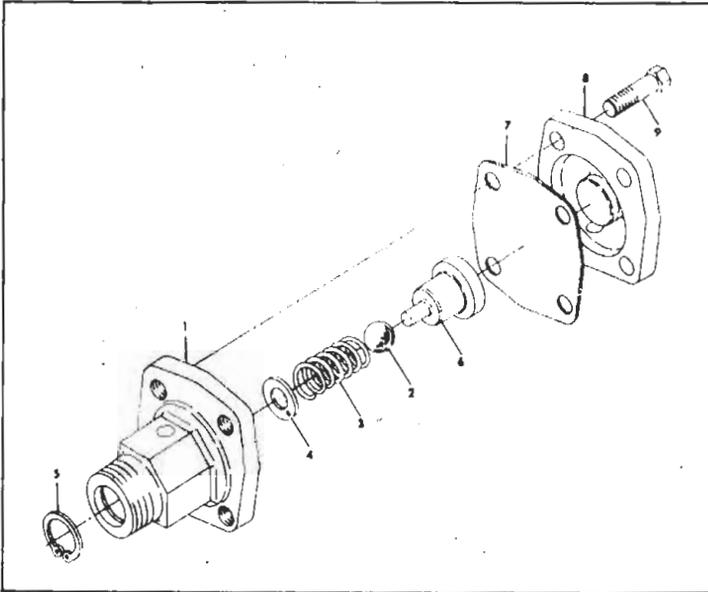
Válvula de descarga automática (INGERSOLL RAND). 1.- Cuerpo de válvula. 2.- Esfera. 3.- Muelle. 4.- Asiento del muelle. 5.- Frenillo. 6.- Embolo. 7.- Membrana. 8.- Soporte. 9.- Tornillo.
